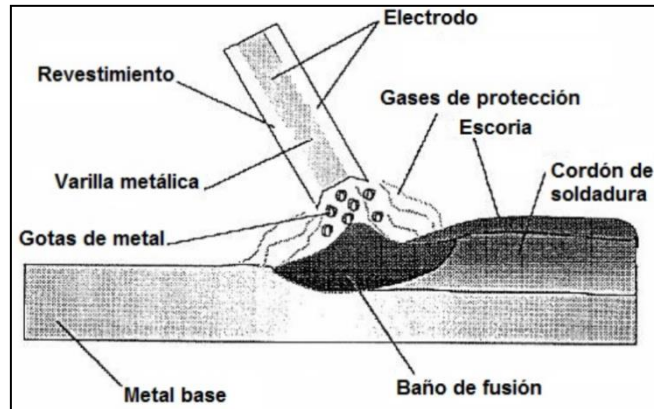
Generalidades de soldadura por arco electrodo revestido tomado de <https://ingemecanica.com/tutorialsemanal/tutorialn45.html>
